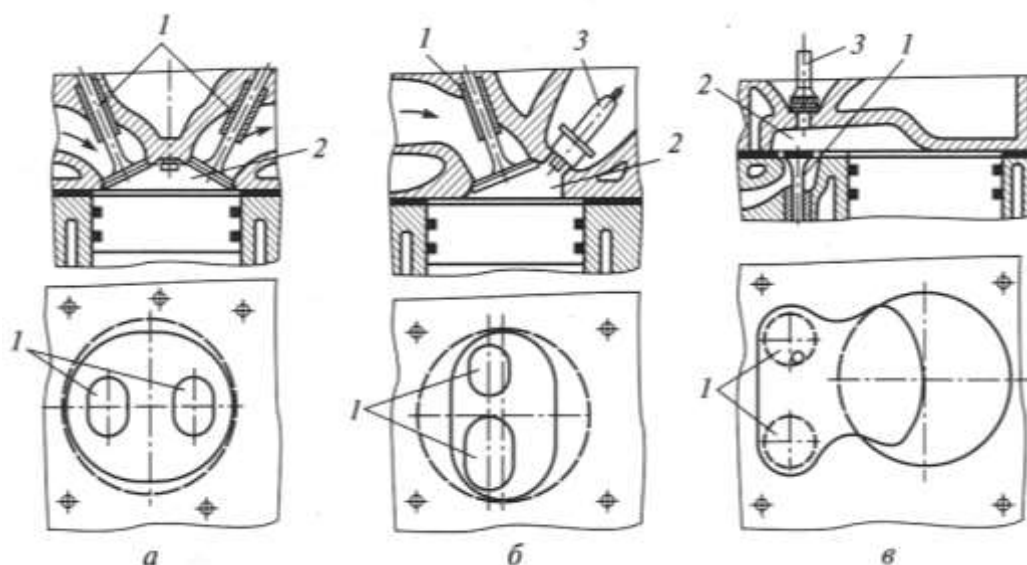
Формы камер сгорания карбюраторных двигателей: а — полусферические; б — полуклиновые; в — смешанные; 1 — клапаны; 2 — камеры сгорания; 3 — свечи зажигания.
